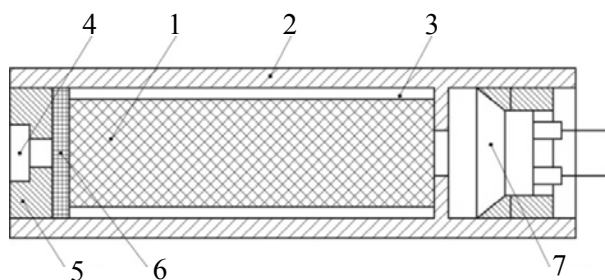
Конструктивная схема пиротехнического газогенератора: 1 – газогенерирующий заряд; 2 – корпус; 3 – зазор; 4 – канал вывода газа; 5 – гайка; 6 – фильтрующий элемент; 7 – иницирующее устройство
